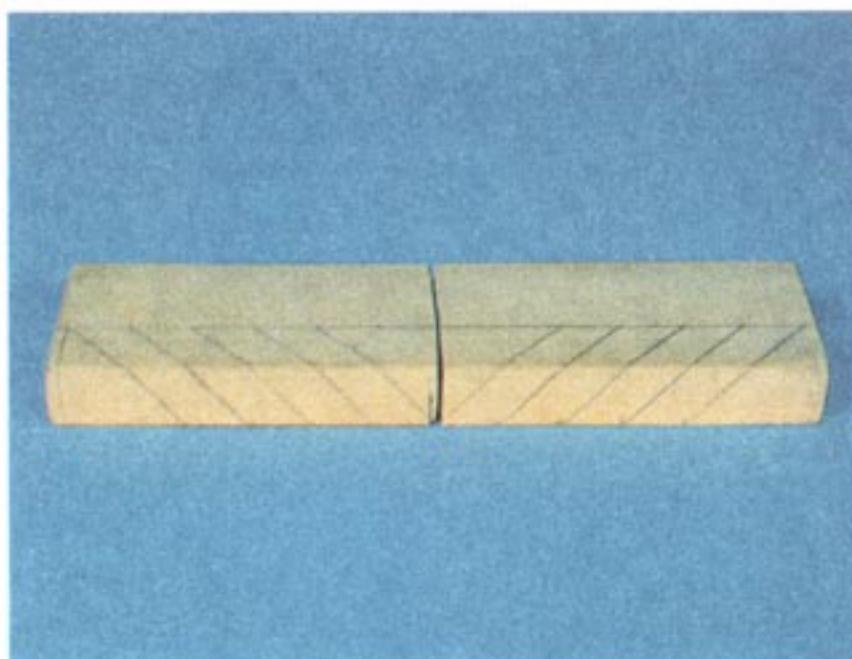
Соединение точек при правой (левая заготовка) и левой разметках
